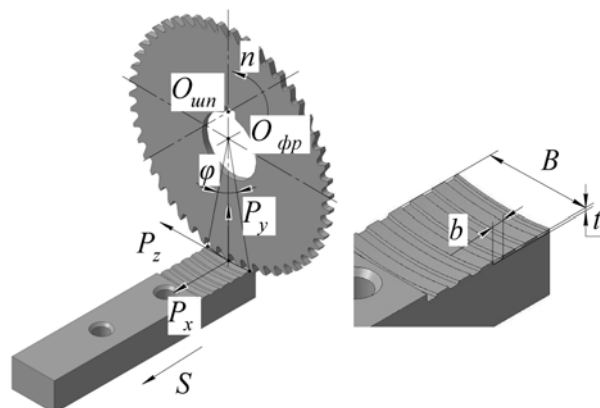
Імітаційна модель процесу контурної обробки зубчастих ланок дисковим інструментом
